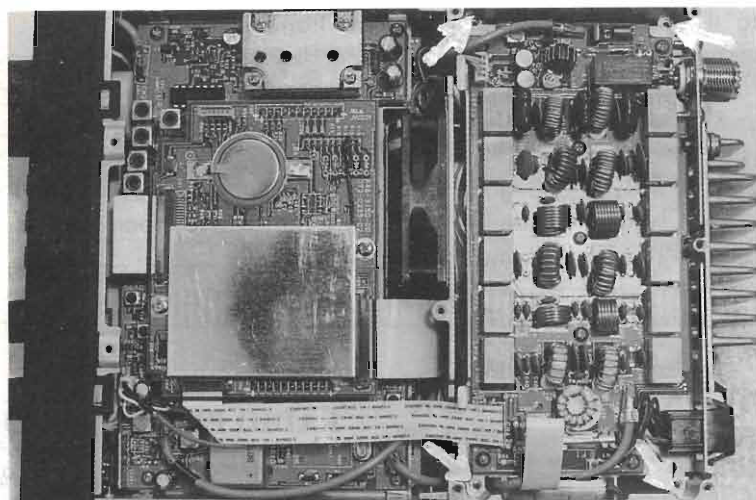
Lato inferiore dell'RTX senza le 4 viti di fissaggio del telaio relè+filtri.
